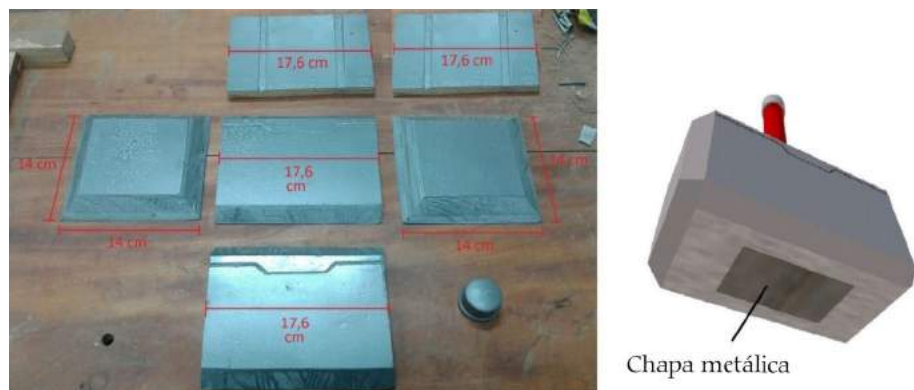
Dimensões do Mjölñir e perspectiva 3D.
